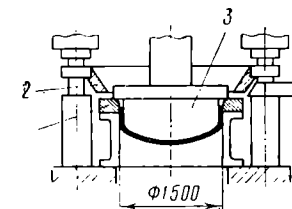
Штамп для вытяжки крупных деталей типа днищ
